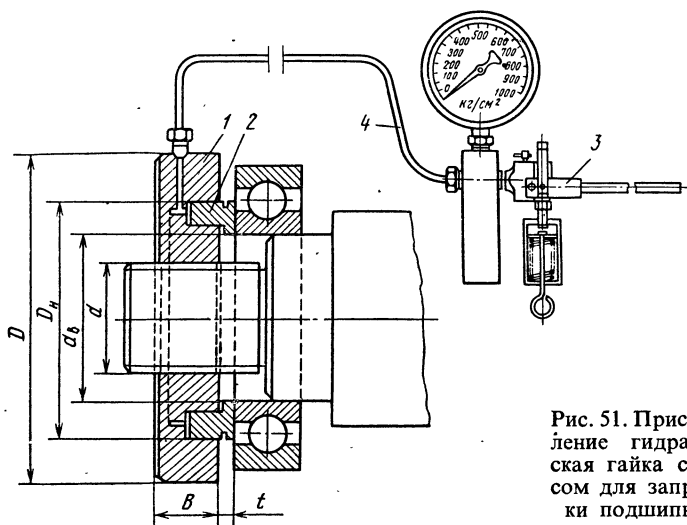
Приспособление гидравлическая гайка с насосом для запрессовки подшипников
